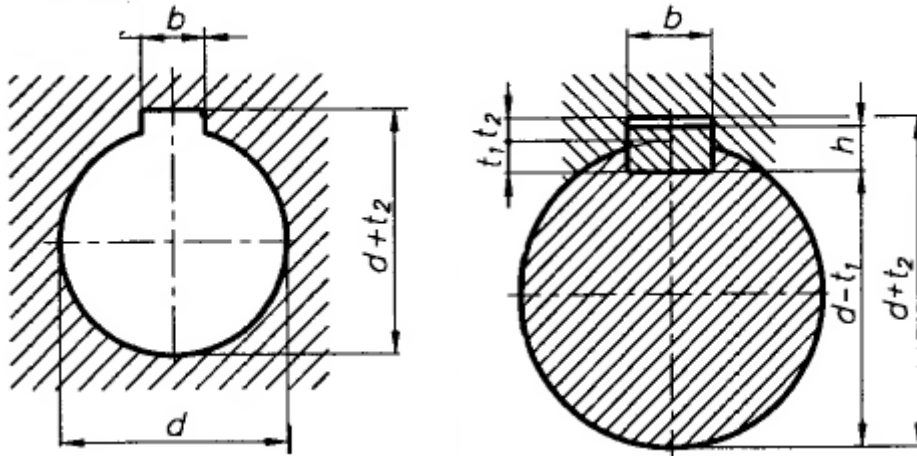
Схема расположения шпоночного паза на зубчатом колесе
